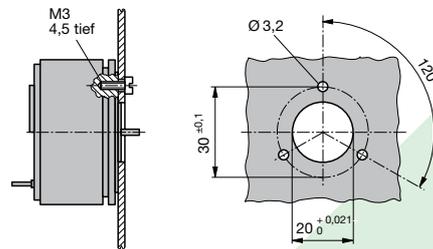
Bohrplan für Befestigung mit 3 Zylinderschrauben M3.
